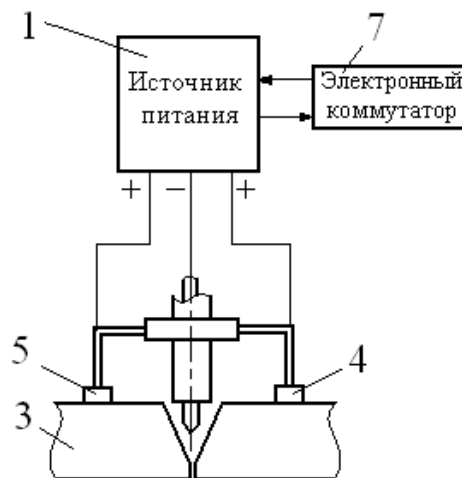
Схема устройства для подвода тока к каждой из свариваемых кромок
